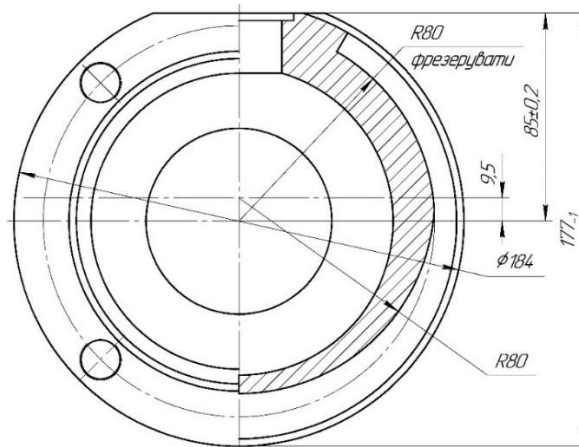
Нетехнологічний елемент деталі – ексцентрична поверхня
